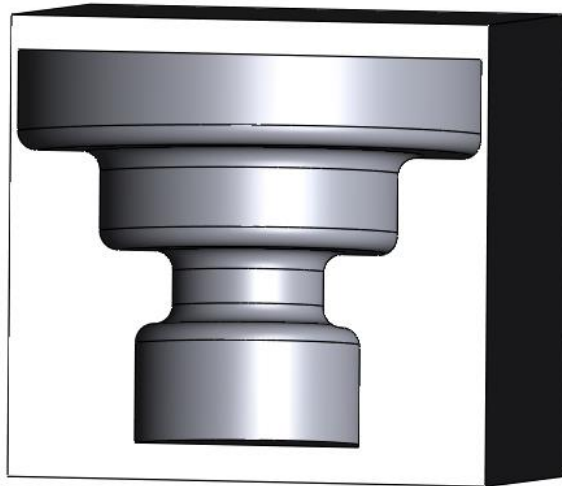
Imagen del CAD del segundo tipo de soporte diseñado para la fabricación de la pieza 7.
